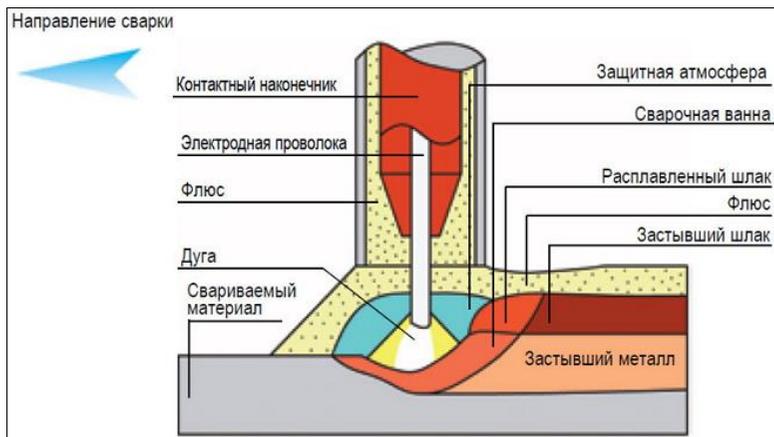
Схема сварки под слоем флюса
